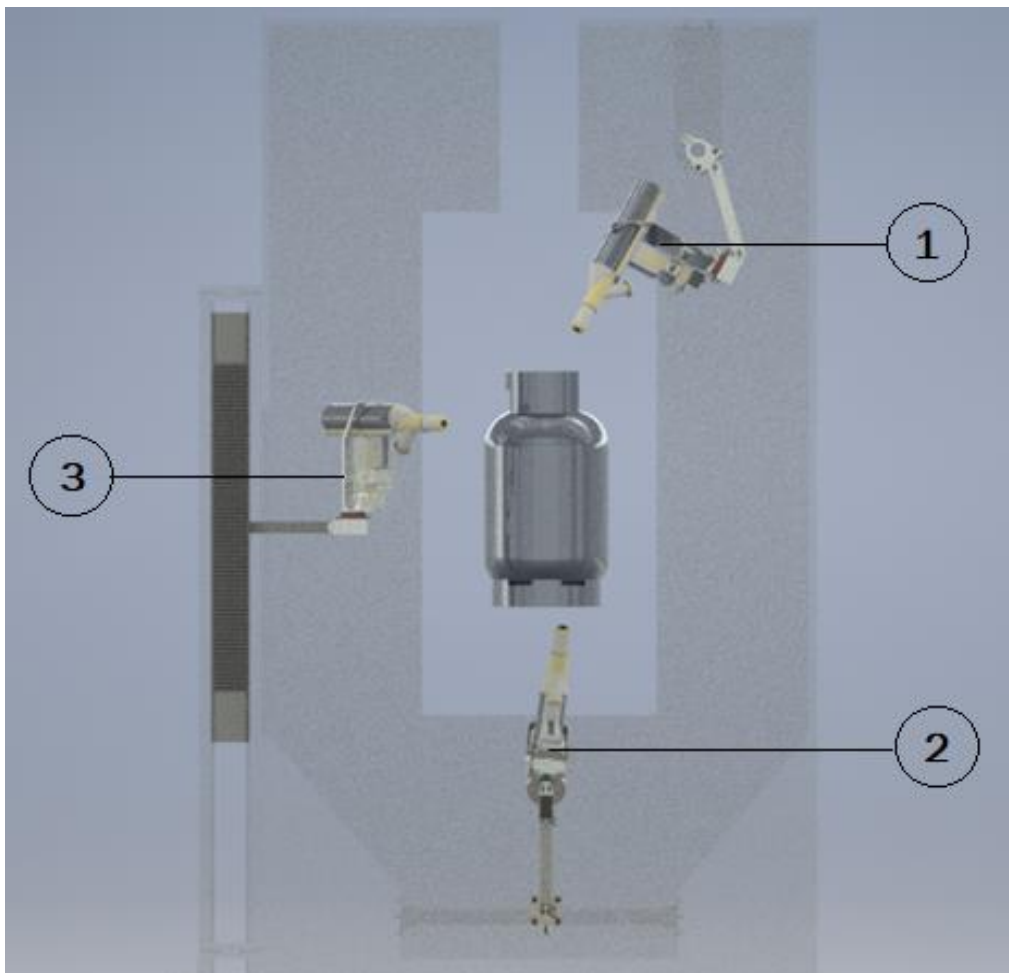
Ensamble total del sistema en vista frontal. [Autor]
